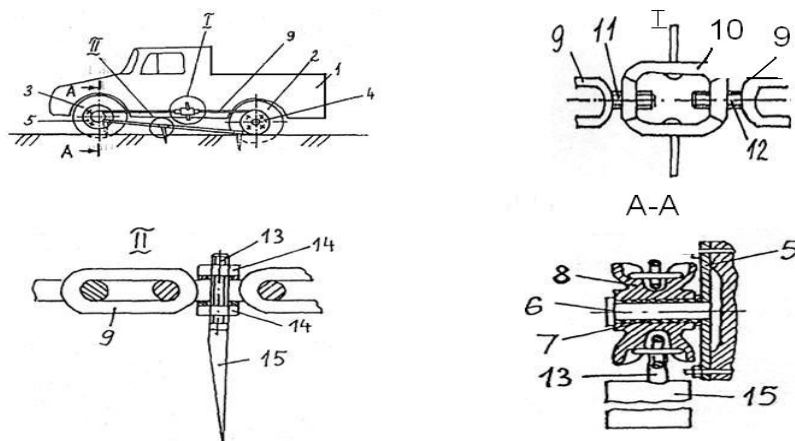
Устройство, устанавливаемое на транспортное средство для самовытаскивания: 1 - транспортное средство; 2- ведущие задние колеса; 3- ведомые передние колеса; 4- задний накладной диск; 5- передний накладной диск; 6- ось; 7- подшипник; 8- звездочка; 9- цепь; 10- винтовая стяжка; 11- винт с левой резьбой; 12- винт с правой резьбой; 13- стержень; 14- гайка; 15 - грунтозацеп
